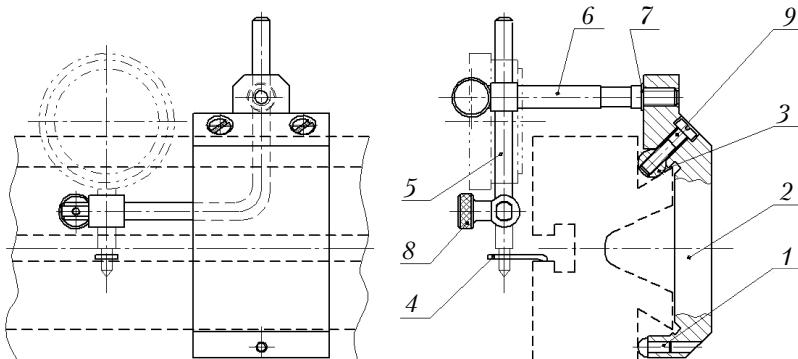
Эскиз приспособления для контроля отклонения от параллельности поверхностей ласточкиного хвоста относительно паза стола фрезерного станка
